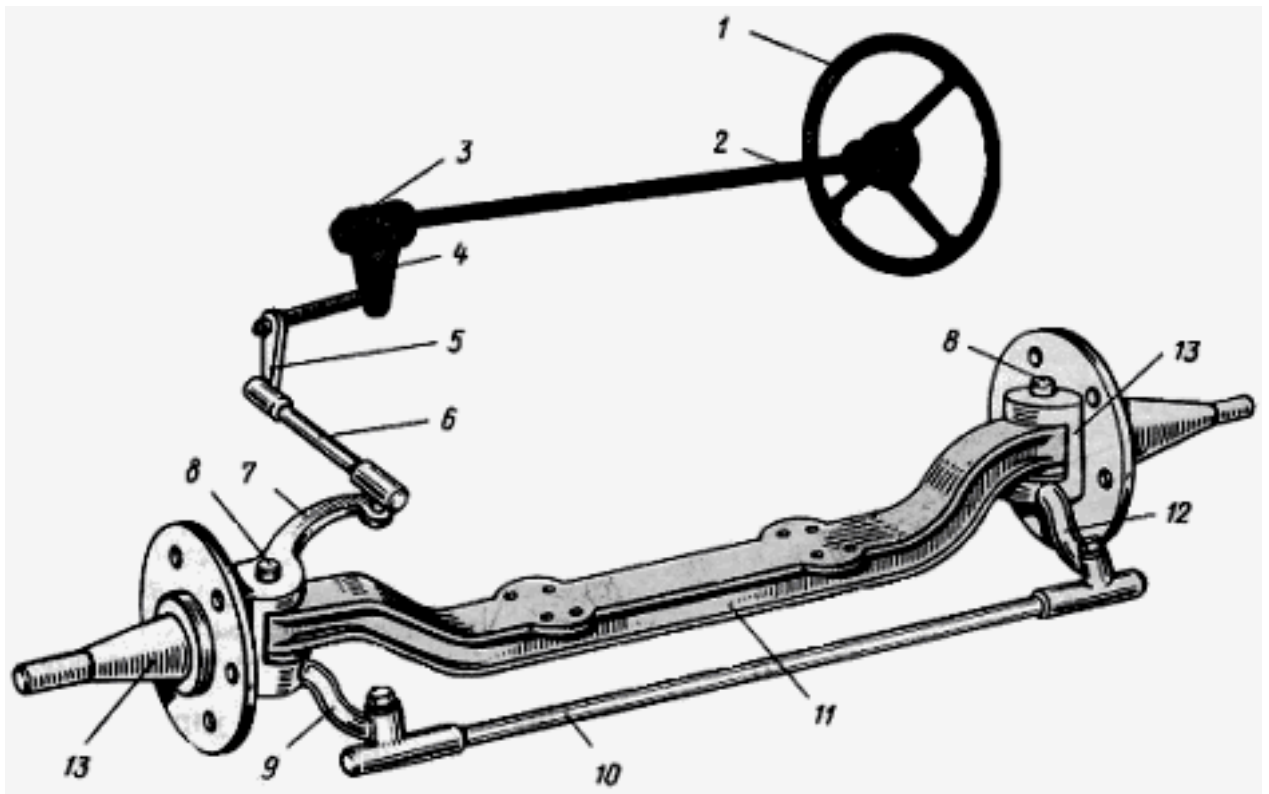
Схема рулевого управления: 1 - рулевое колесо; 2 - вал; 3 - червяк; 4 - сектор; 5 - сошка; 6 - продольная тяга; 7, 9, 12 - рычаг; 8 - шкворень; 10 - поперечная тяга; 11 - балка; 13 - поворотная цапфа
